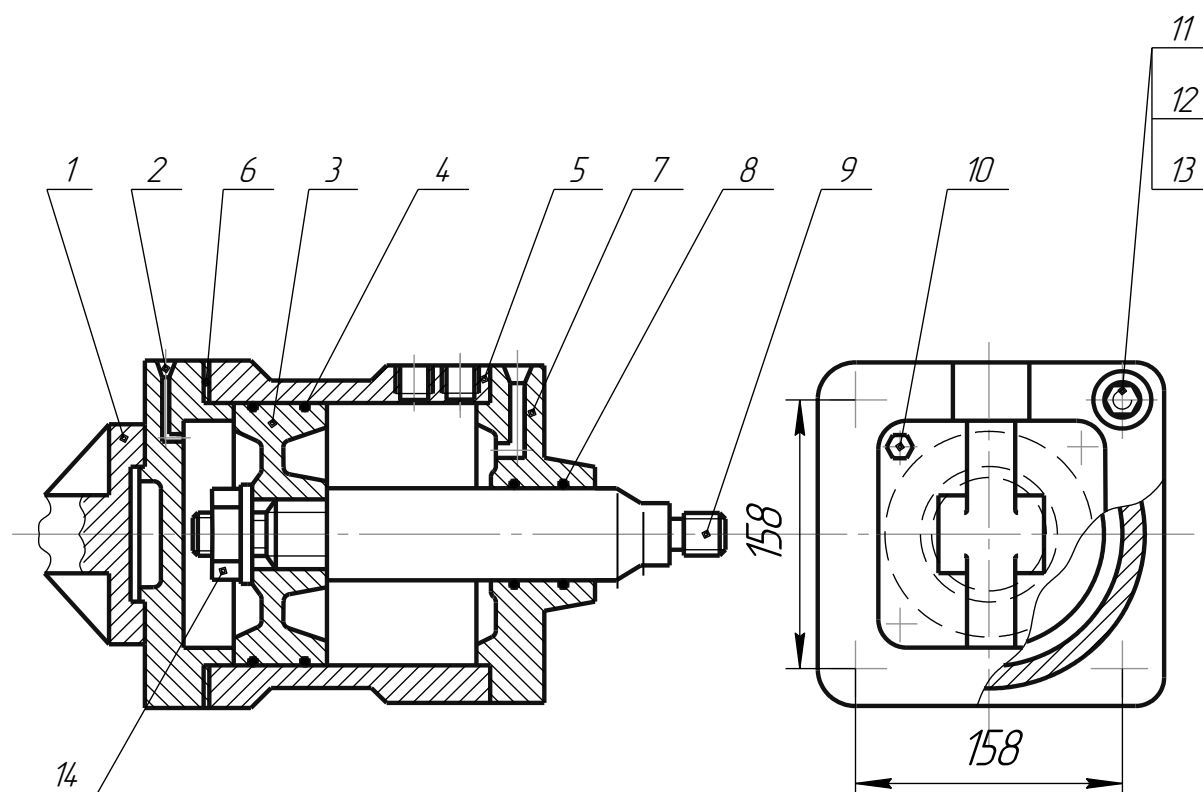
Пневмоциліндр для верстатних пристроїв
